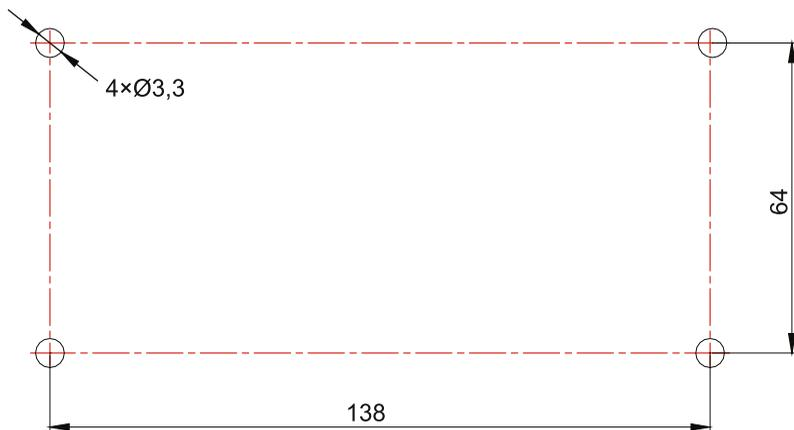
Ouvertures pour montage des boîtiers d'installation
